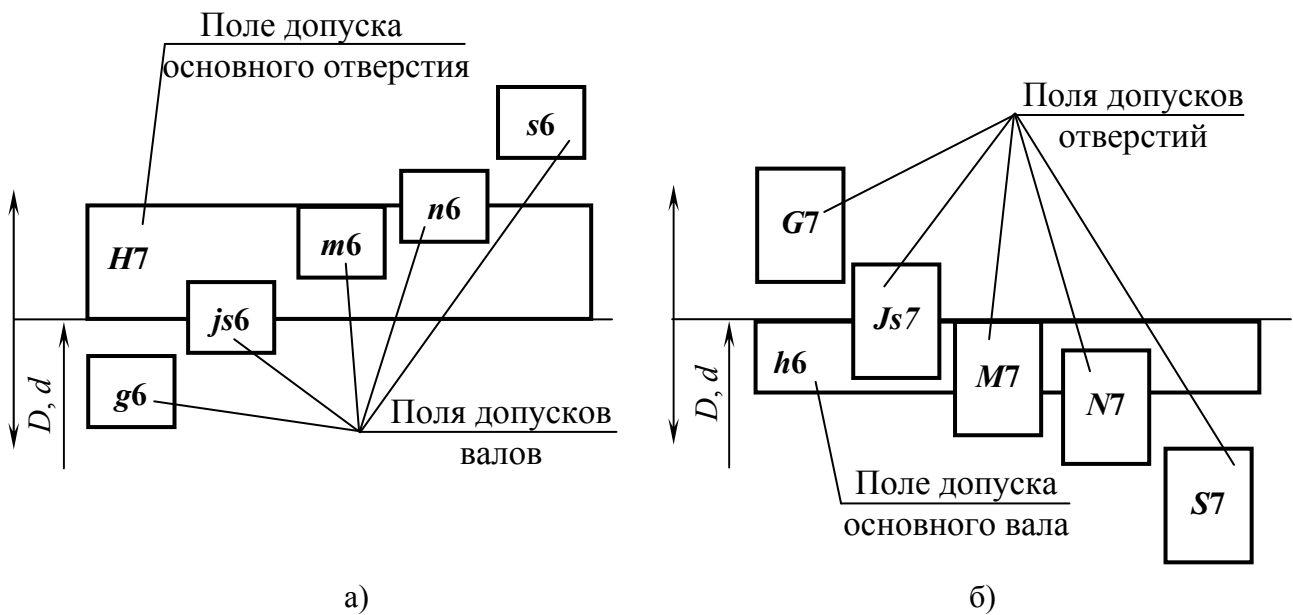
Схемы расположения полей допусков отверстий и валов:
